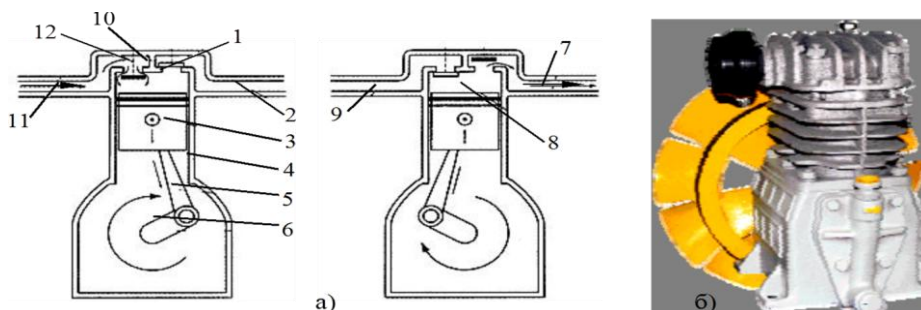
Принцип дії (а) та зовнішній вигляд (б) поршневого компресора: 1, 12 – нагнітальний та всмоктувальний клапани; 2, 7 – нагнітальна лінія; 3 – поршень; 4 – корпус; 5 – шток; 6 – вал; 8 – робоча камера; 9, 11 – всмоктувальна лінія; 10 – перегородка.
